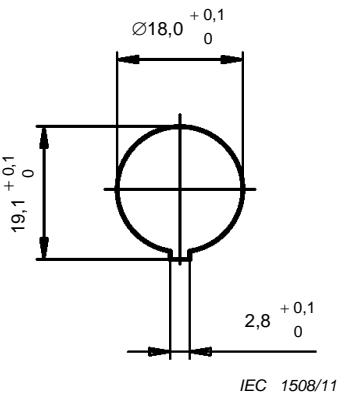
Dimensions – Plan de découpe des panneaux IP40
